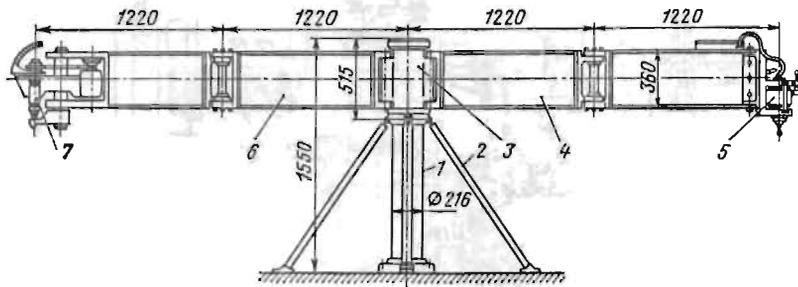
Радиальный сверлильно-фрезерный станок РСФ
